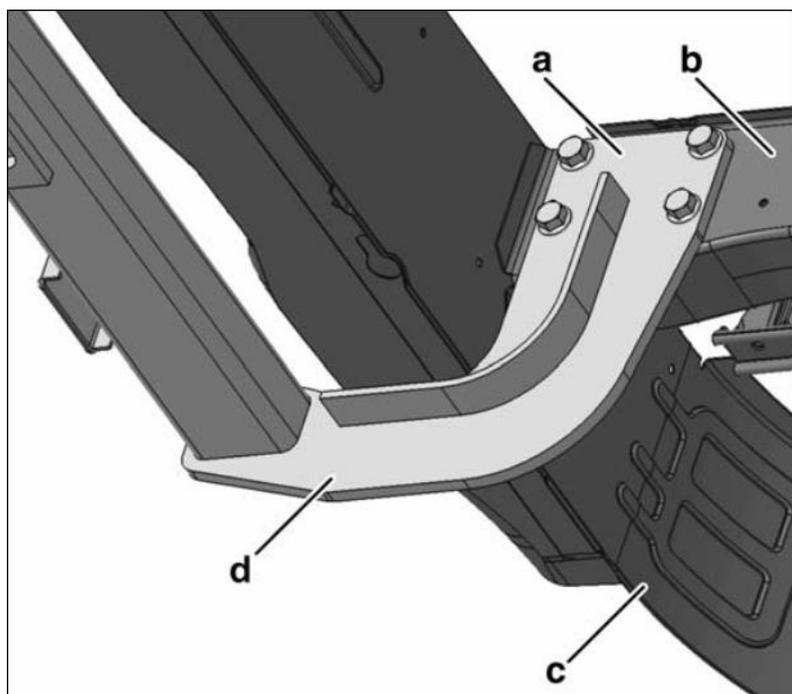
traversa terminale del longherone destro del telaio dall'interno
